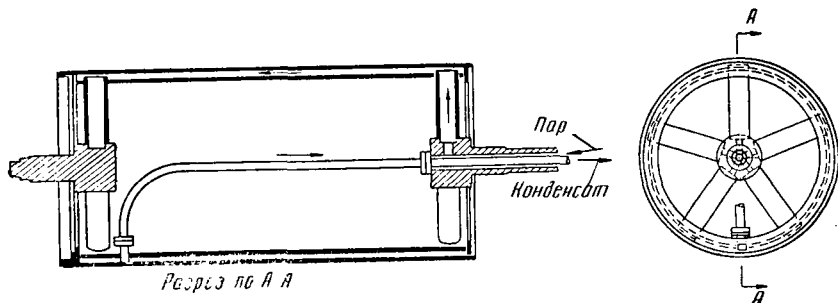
Стальной сушильный цилиндр с двойными стенками
